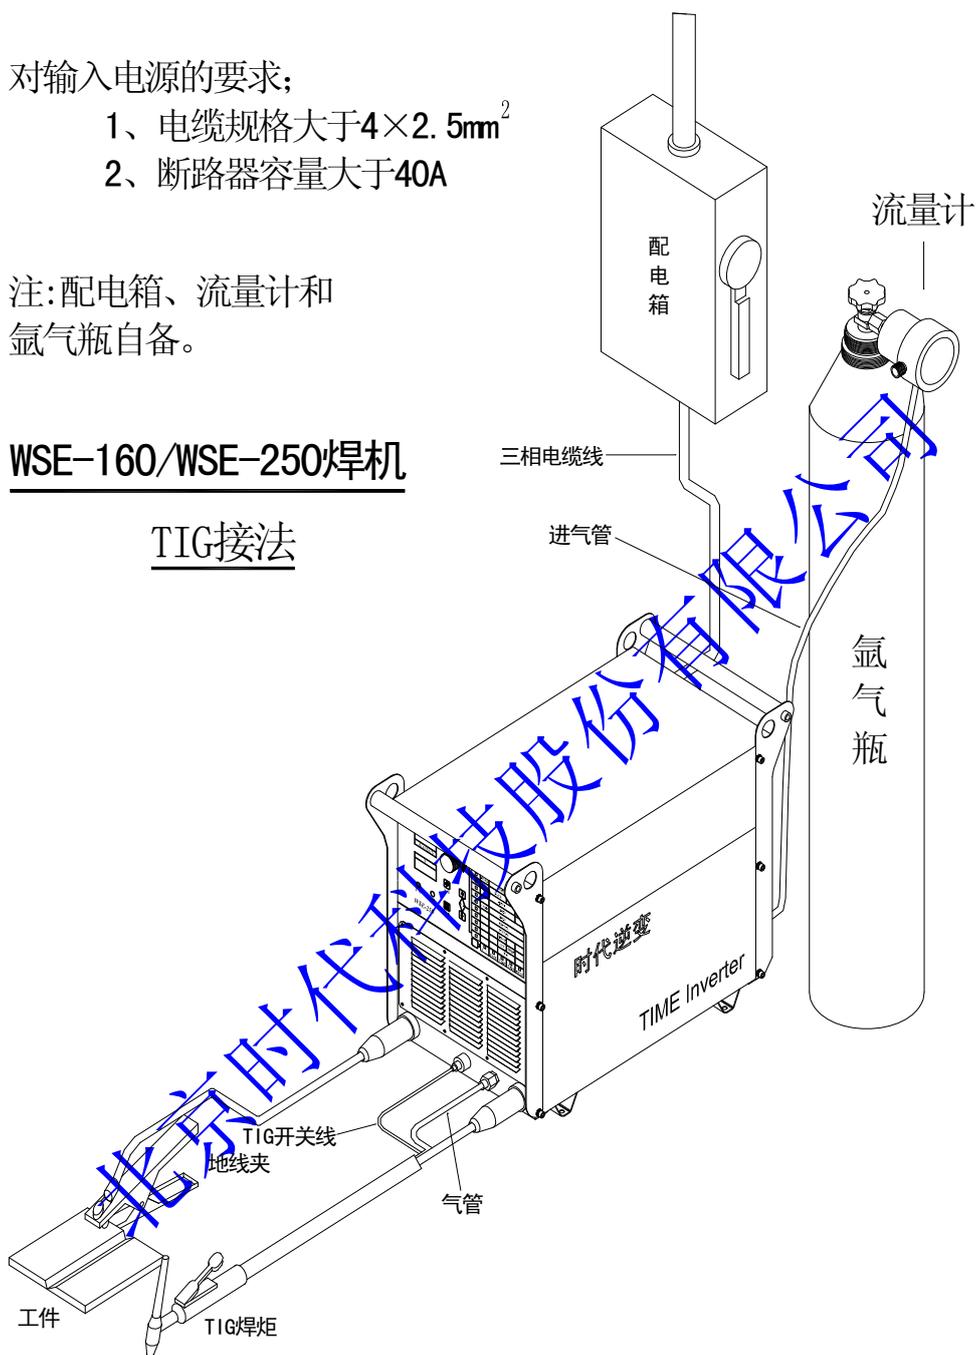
A WSE-160/WSE-250 焊机的 TIG 接法
